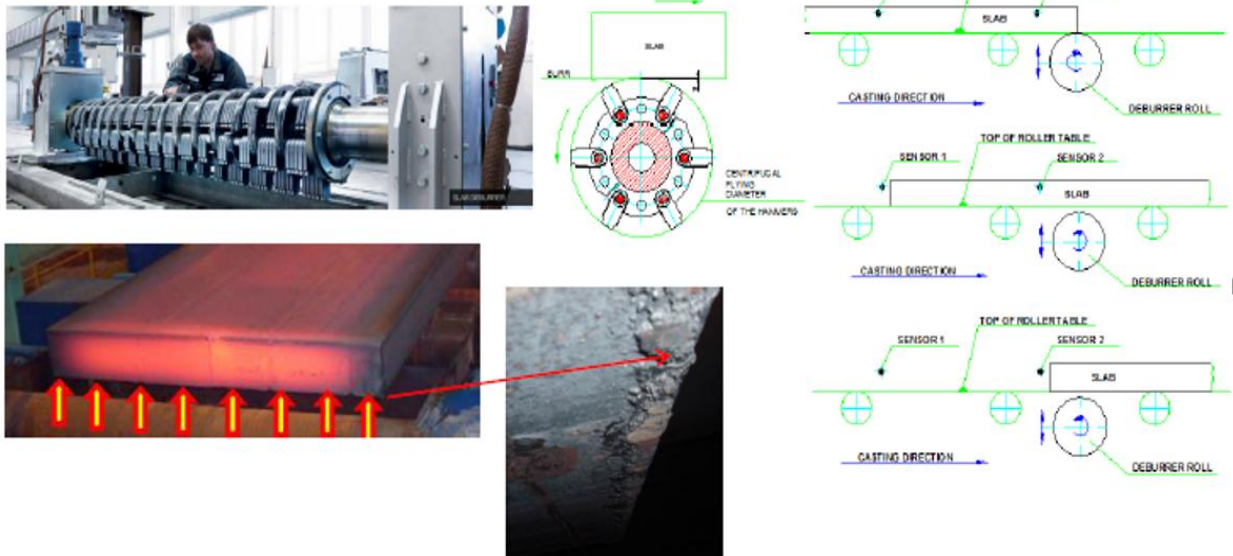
Машина для видалення задирок (Deburring Machine)
